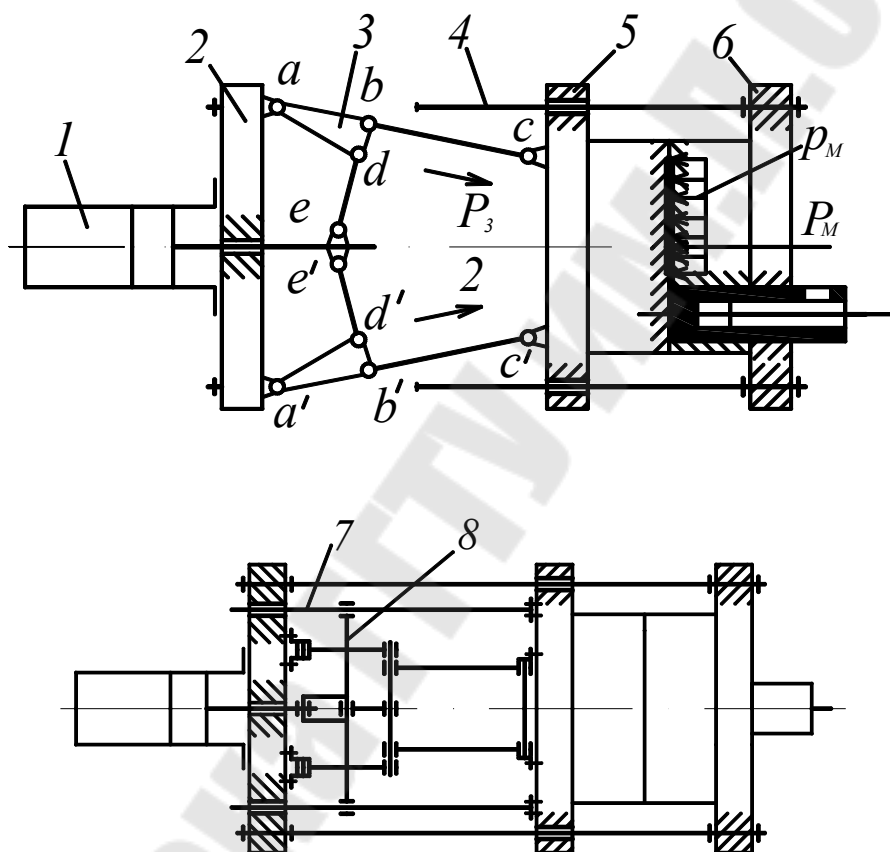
Общая схема рычажного запирающего механизма: 1 - гидроцилиндр; 2, 6 - неподвижные плиты; 3 - рычажный механизм; 4 - направляющая; 5 - подвижная плита; 7 - направляющее уравнивающее устройство; 8 - траверса
